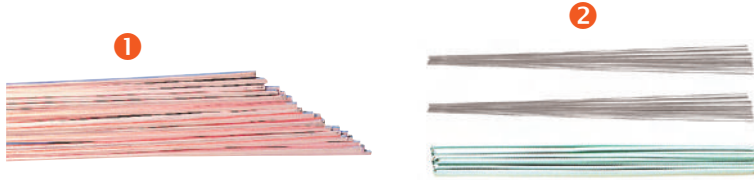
Ejemplos de varillas de soldadura fuerte (soldadura)
